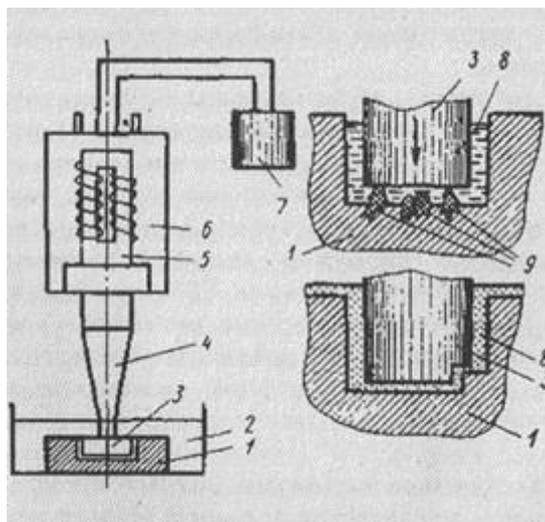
Схема ультразвуковой размерной обработки (прошивание): 1 - обрабатываемая деталь; 2 - ванна; 3 - инструмент; 4 - акустический трансформатор скорости; 5 - магнестрикционный преобразователь; 6 - корпус с охлаждением; 7 - ультразвуковой генератор; 8 - зазор; 9 - частички абразива
